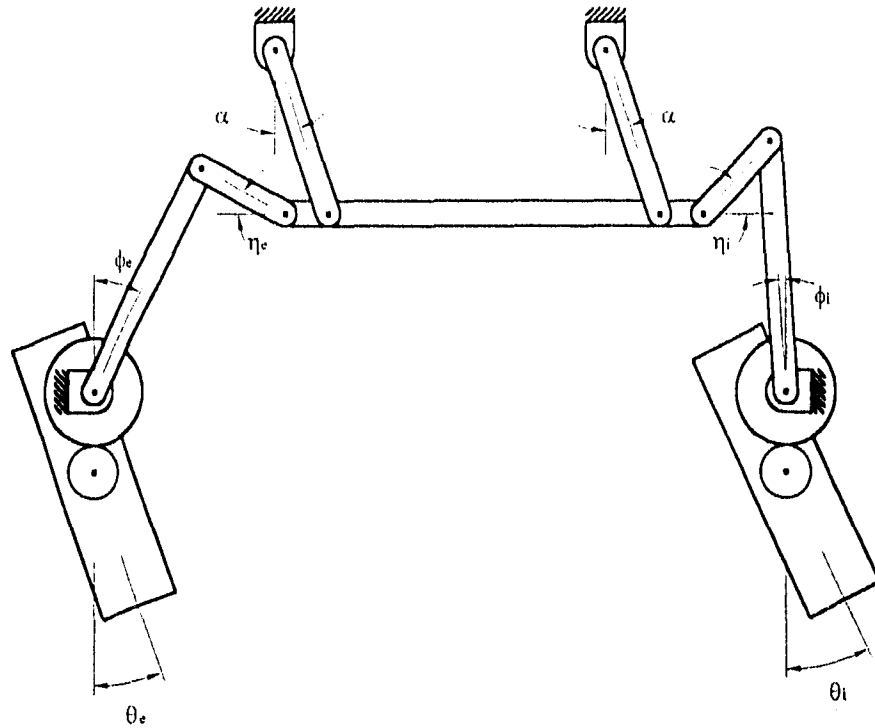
Ángulos del mecanismo. Posición vuelta a la izquierda.
